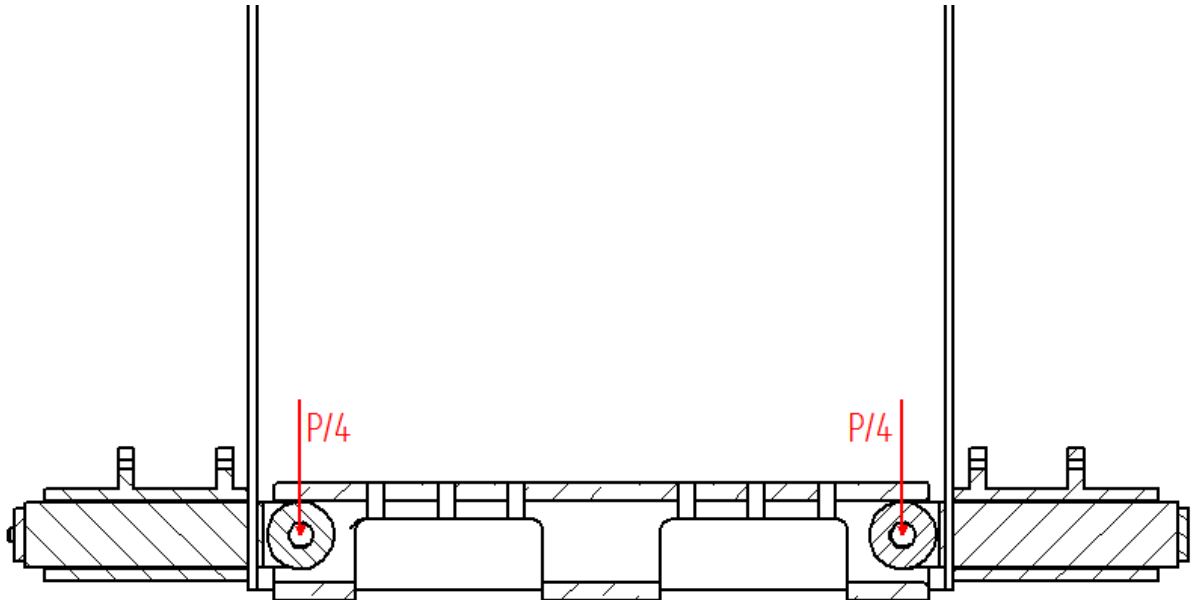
vista in sezione del sistema di sollevamento dei pallet
